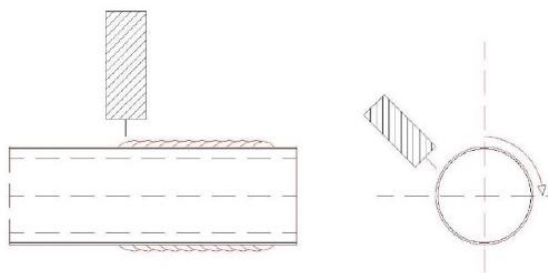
Esquema de aplicação de revestimento weld overlay
